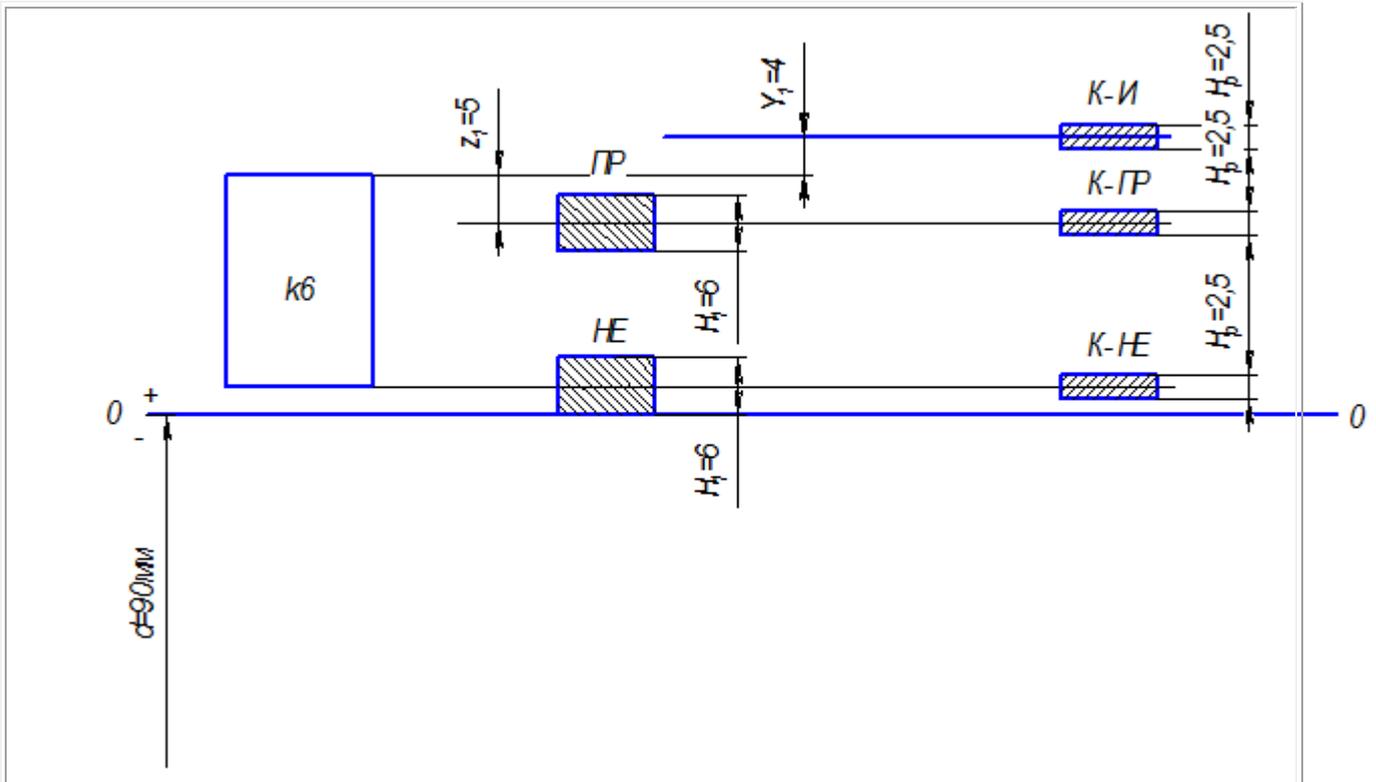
Схема расположения полей допусков калибров и контрокалибров для $d=90k6$
